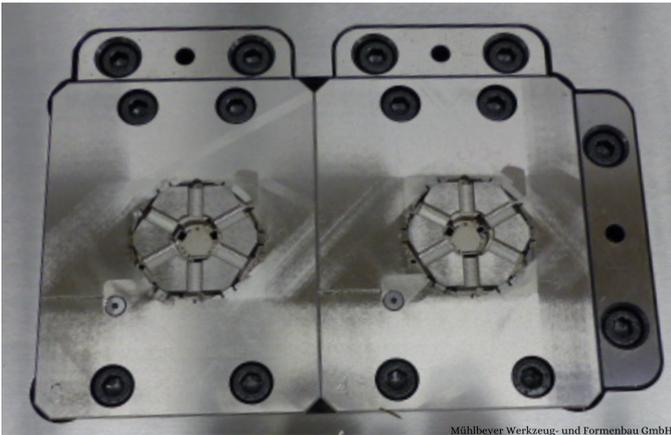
Spritzgießwerkzeug 1-fach Düsenseite für kunststoffummantelter Stator
